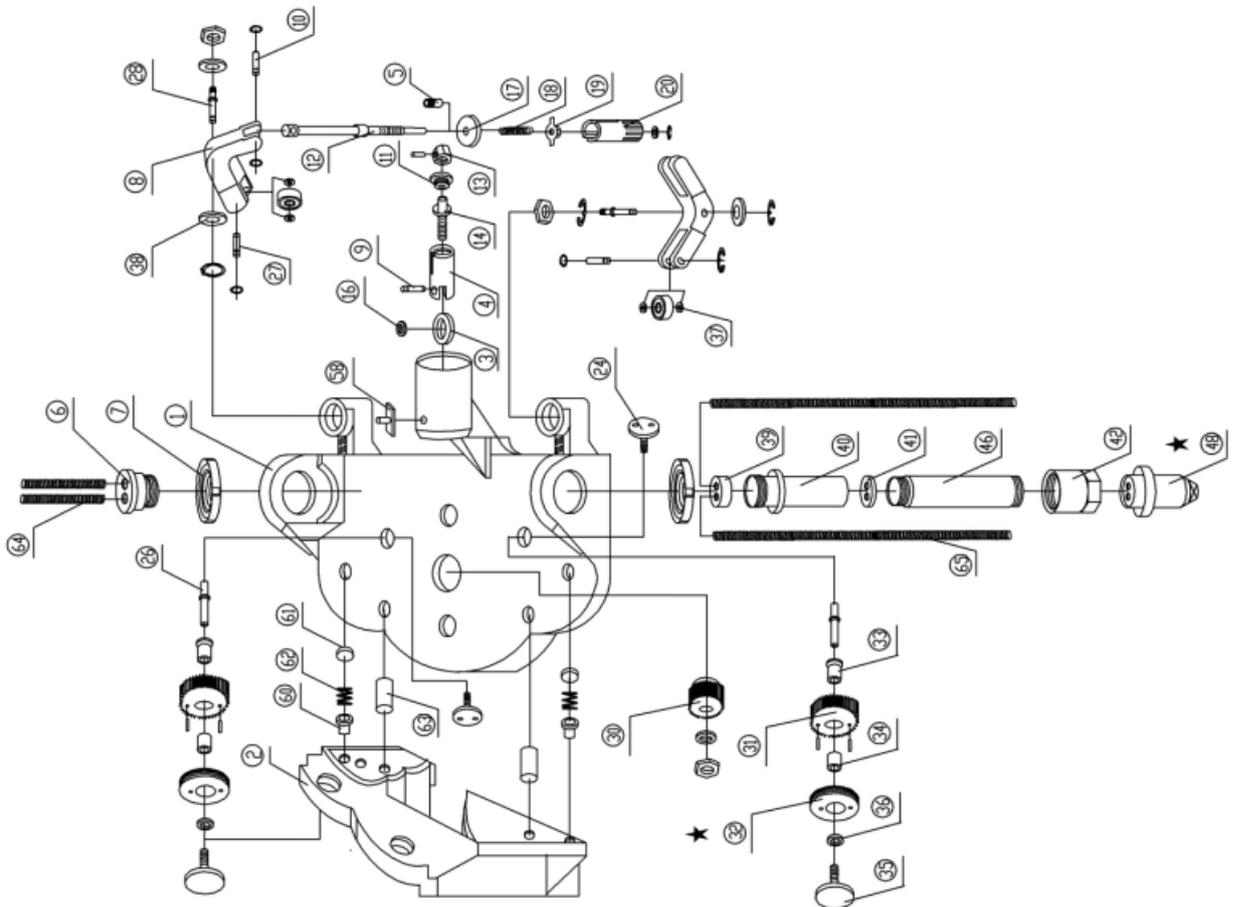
Desmontaje y montaje del soporte de la cabeza del tractor de doble alambre
